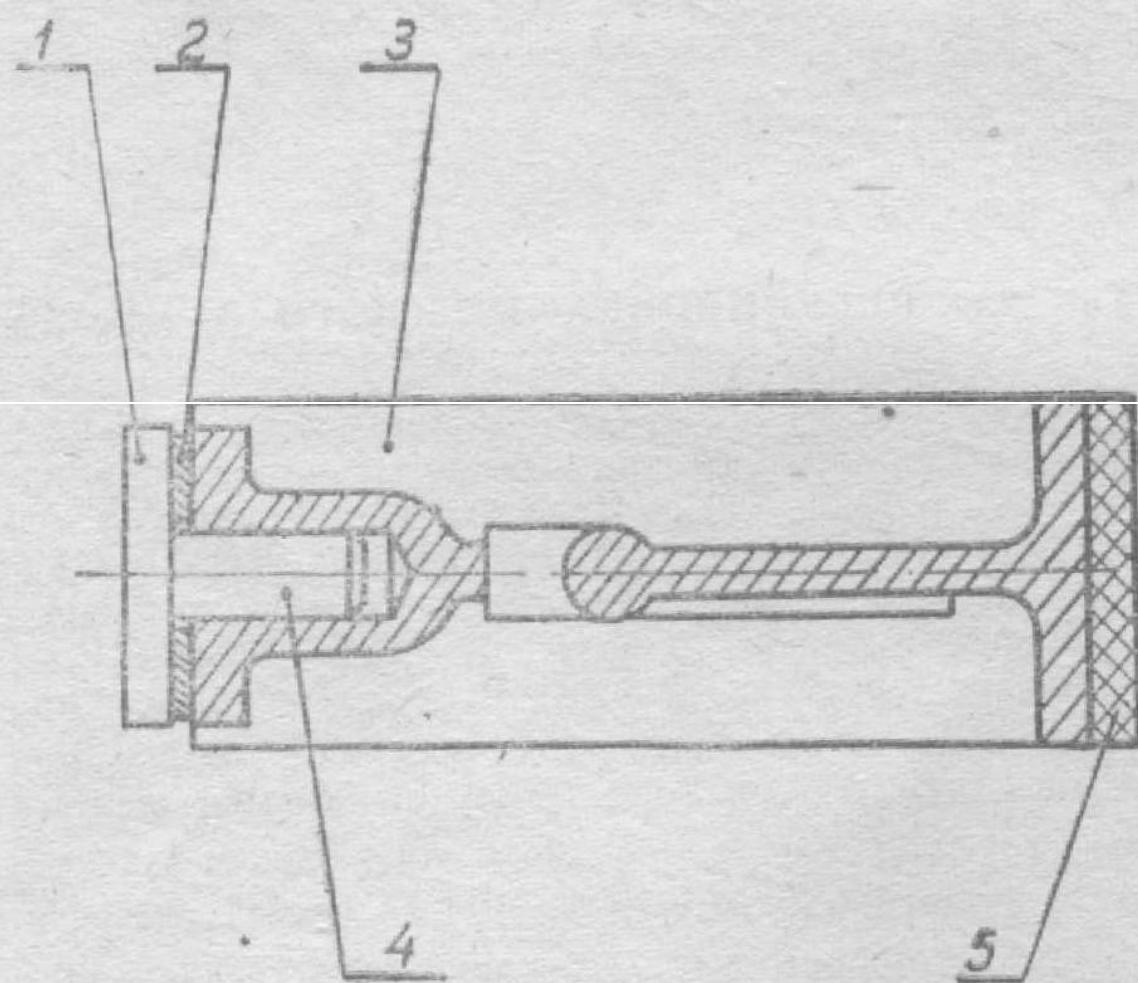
КОЛОДКА ТОРМОЗНАЯ (ЛИТАЯ):
